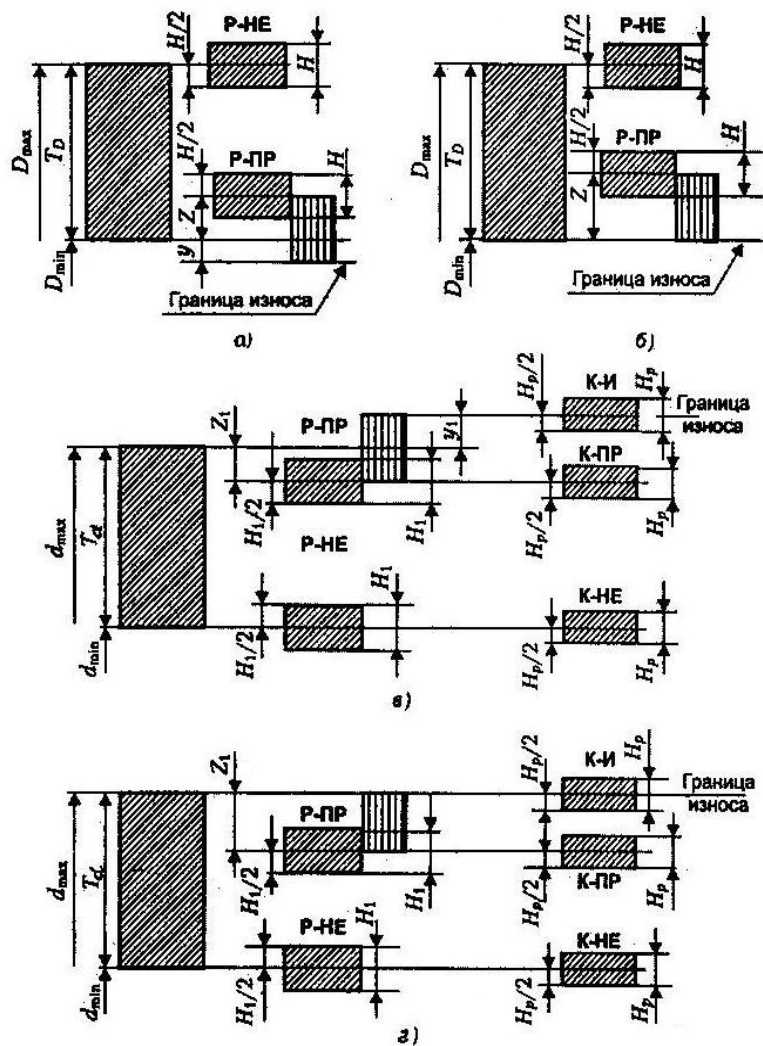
Схемы расположения допусков калибров для номинальных размеров до 180 мм: а – для отверстий IT6–IT8; б – для отверстий IT9–IT17; в – для валов IT6–IT8; г – для валов IT9–IT17.
